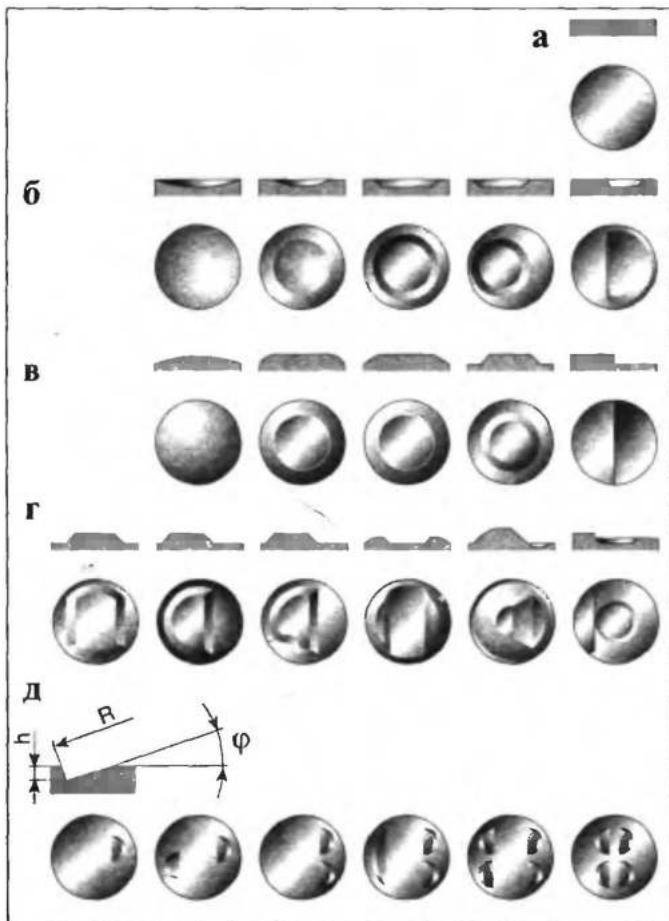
Типовые формы днища поршней бензиновых двигателей: а — плоское; б — с размещением части камеры сгорания в поршне; в — с вытеснителями простой формы; г — с вытеснителями сложной формы и комбинированные; д — цековки для тарелок клапанов и их размещение на днище
